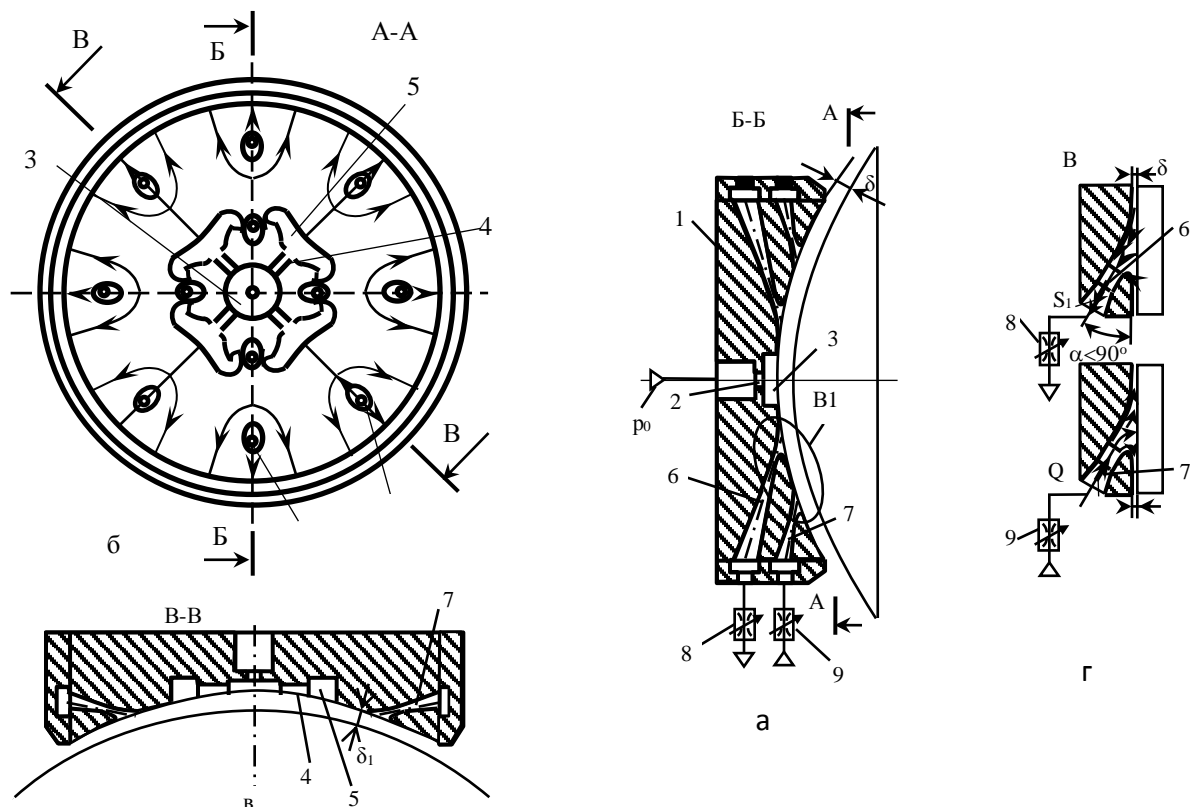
Опорний елемент шарніра із соплами виконаними в корпусі:
